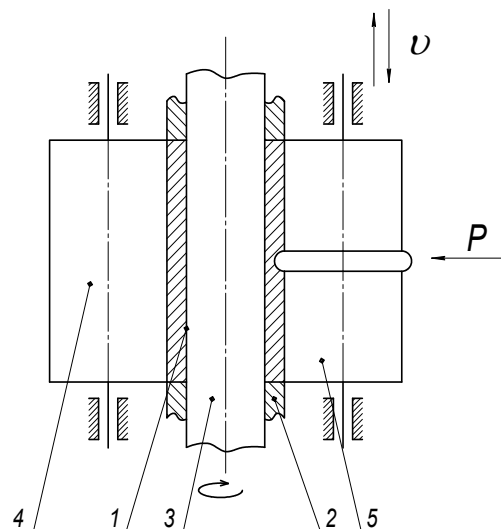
Схема обкатки формирующим и заглаживающим инструментом
